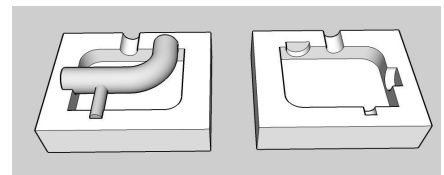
Encaixe do molde interno de parafina no molde externo.
